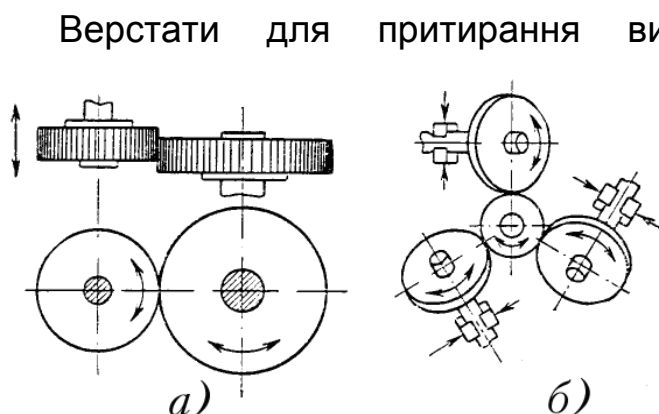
Схеми притирання зубів циліндричних зубчастих коліс:
